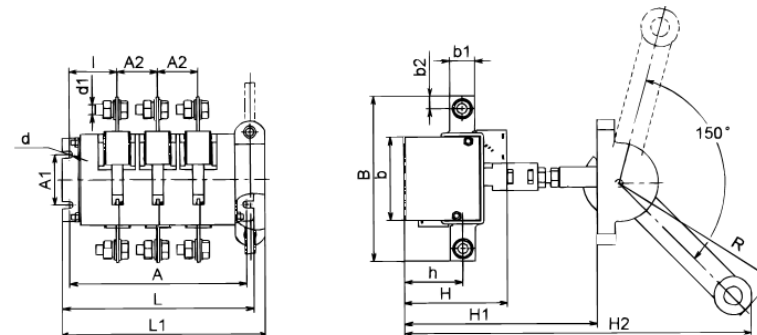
Б Выключатель-разъединитель на одно направление трехполюсный с передней смещенной рукояткой
